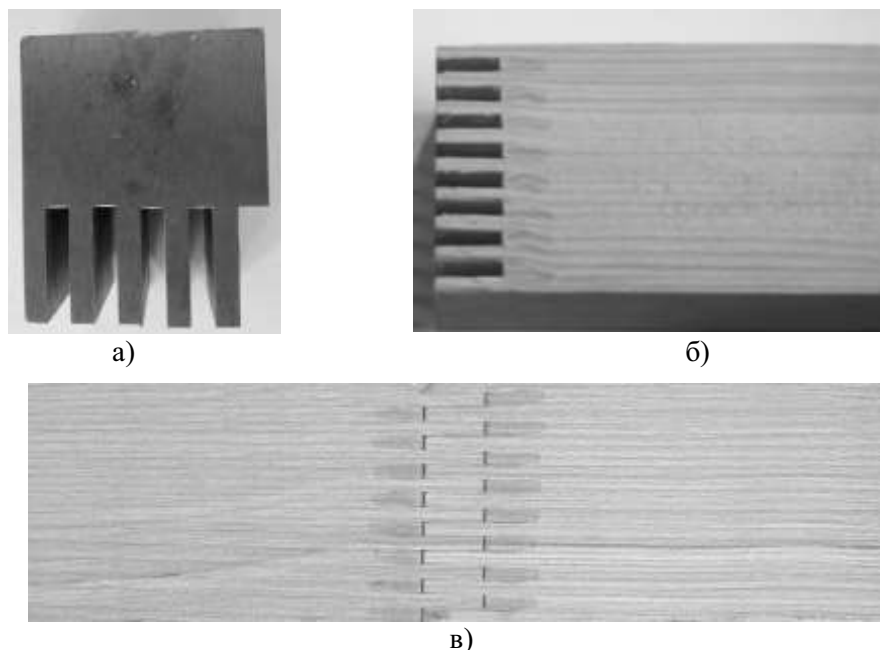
Инструмент для прессования элементов шиповых соединений и обработанные заготовки: а – пуансон для формирования шипов длиной 20 мм, толщиной 4 мм; б – образец заготовки из древесины сосны с шипами длиной 10 мм, толщиной 2 мм; в – фрагмент клеевого соединения по длине на прессованные шипы длиной 10 мм, толщиной 2 мм, заготовки из древесины березы
